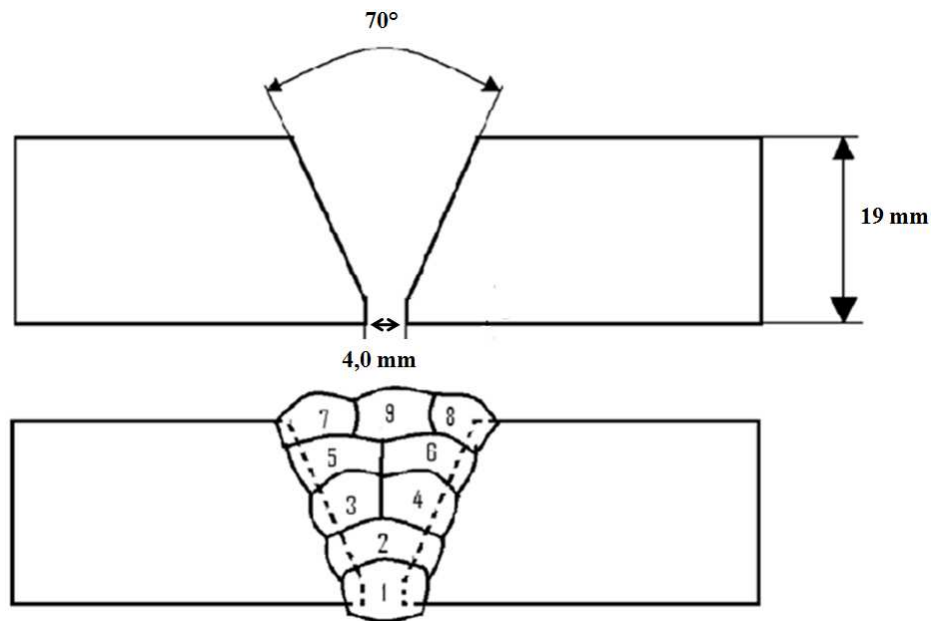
Desenho esquemático da junta a ser soldada e da distribuição de passes de soldagem
